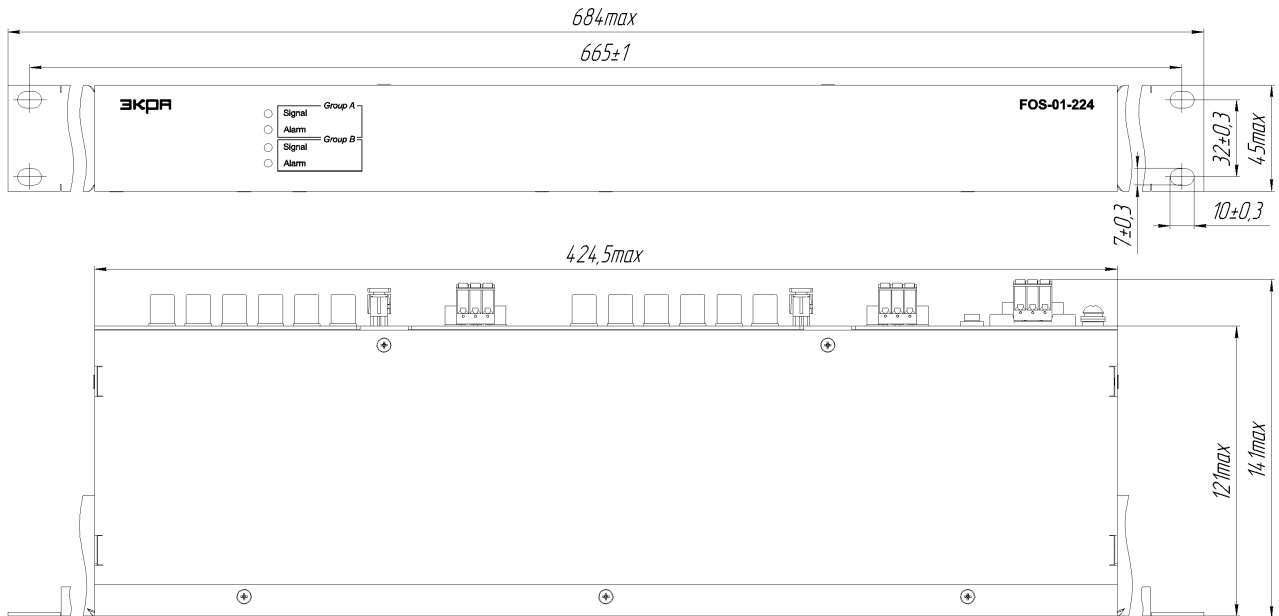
Общий вид разветвителя FOS-01-224-XXX-01
